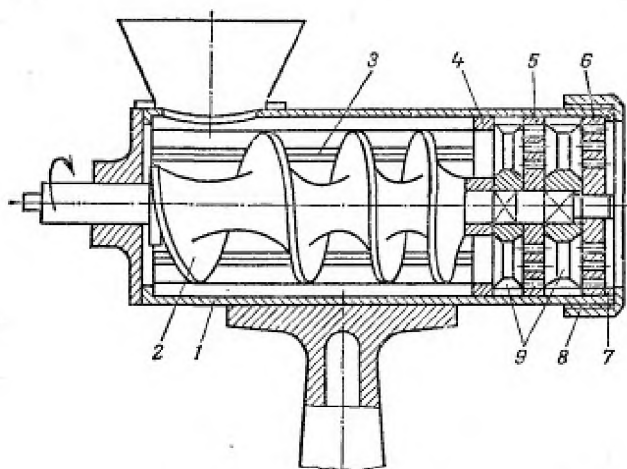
Принципова схема м'ясорубки: 1 – робоча камера; 2 – шнек; 3 – ребра; 4 – решітка підрізна; 5, 6 – решітки ножові; 7 – кільце упорне; 8 – гайка натискна; 9 – ножі
